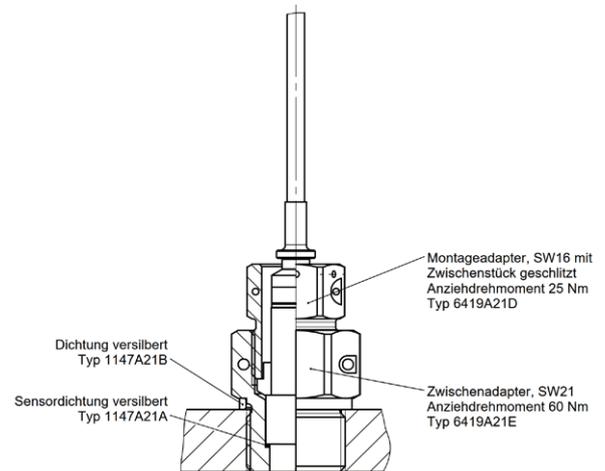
Montage mit Zwischenadapter Typ 6419A21E, Montageadapter Typ 6419A21D sowie Dichtung Typ 1147A21A und Typ 1147A21B
